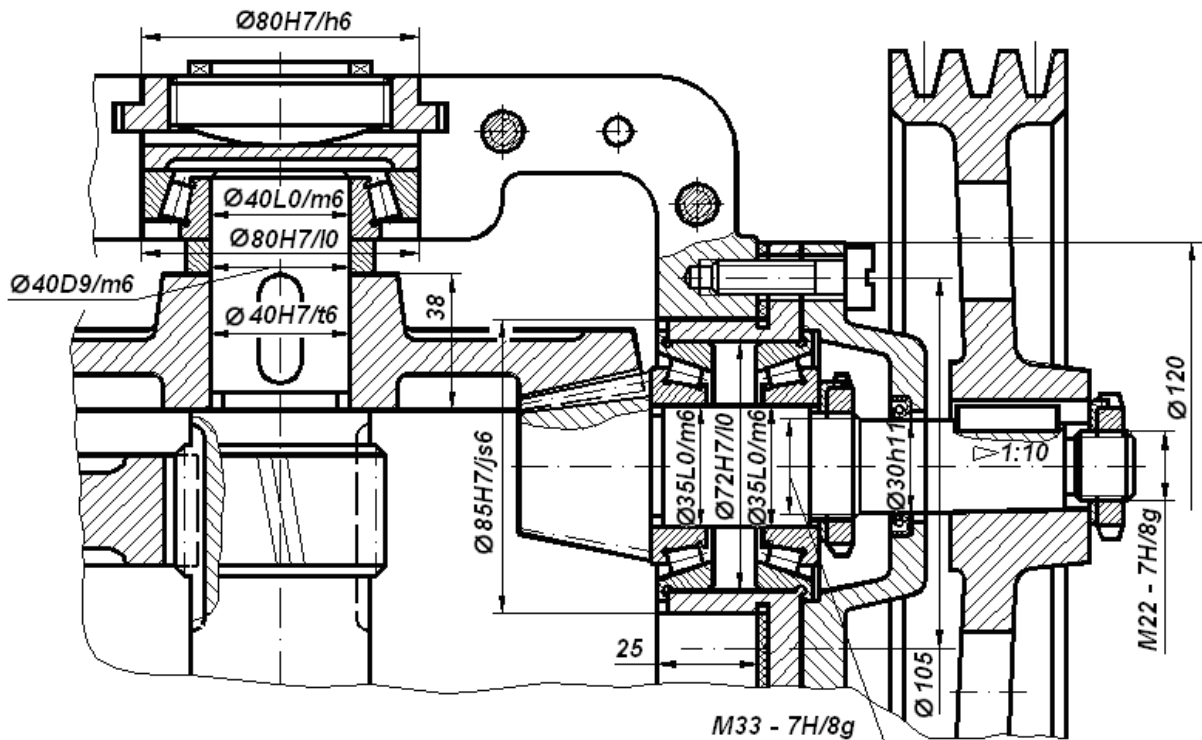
Кресленник конічно-циліндричного редуктора
